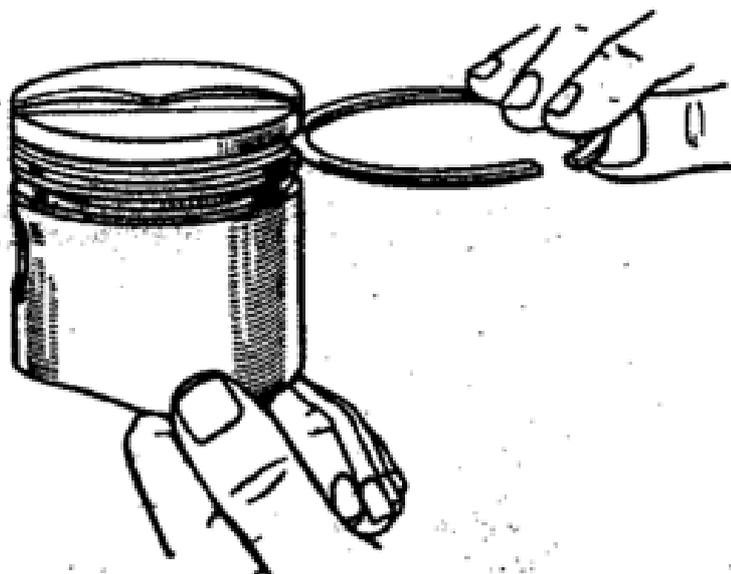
Проверка перемещения поршневого кольца в канавке поршня
